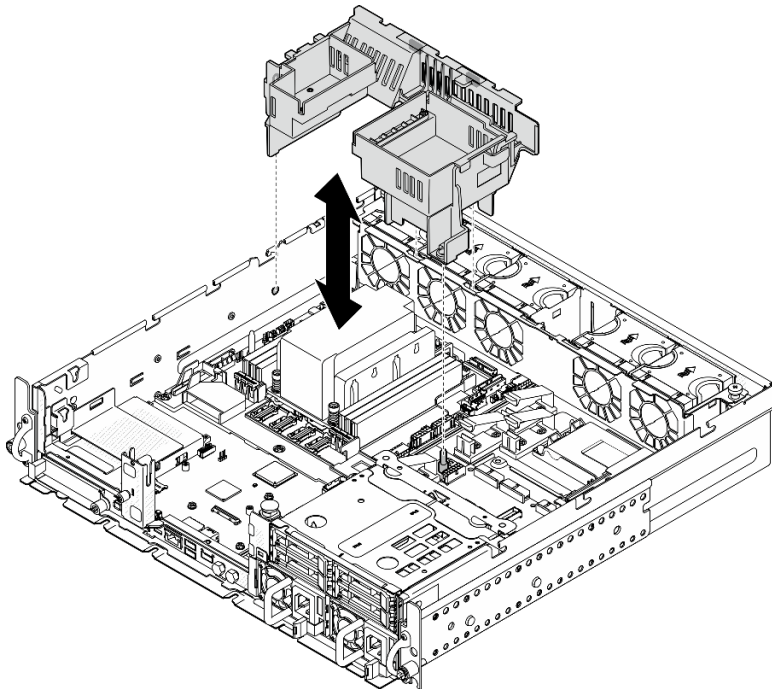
Installation de la grille d'aération pour dissipateur thermique 2U
